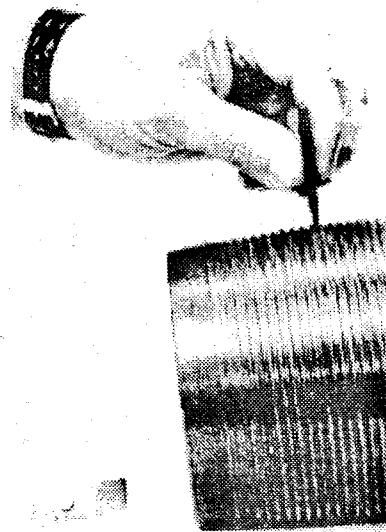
Предельный калибр ширины резьбы безмуфтового соединения
